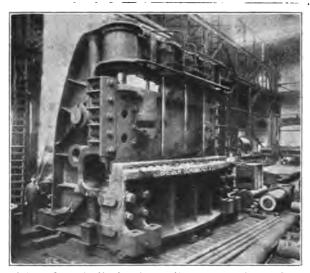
Bobraulische Blechschere für 4 m Breite und 5 cm Dide ber Kalter Wertzeugmaschinensabrit Breuer, Schumacher & Co. A.-G.
